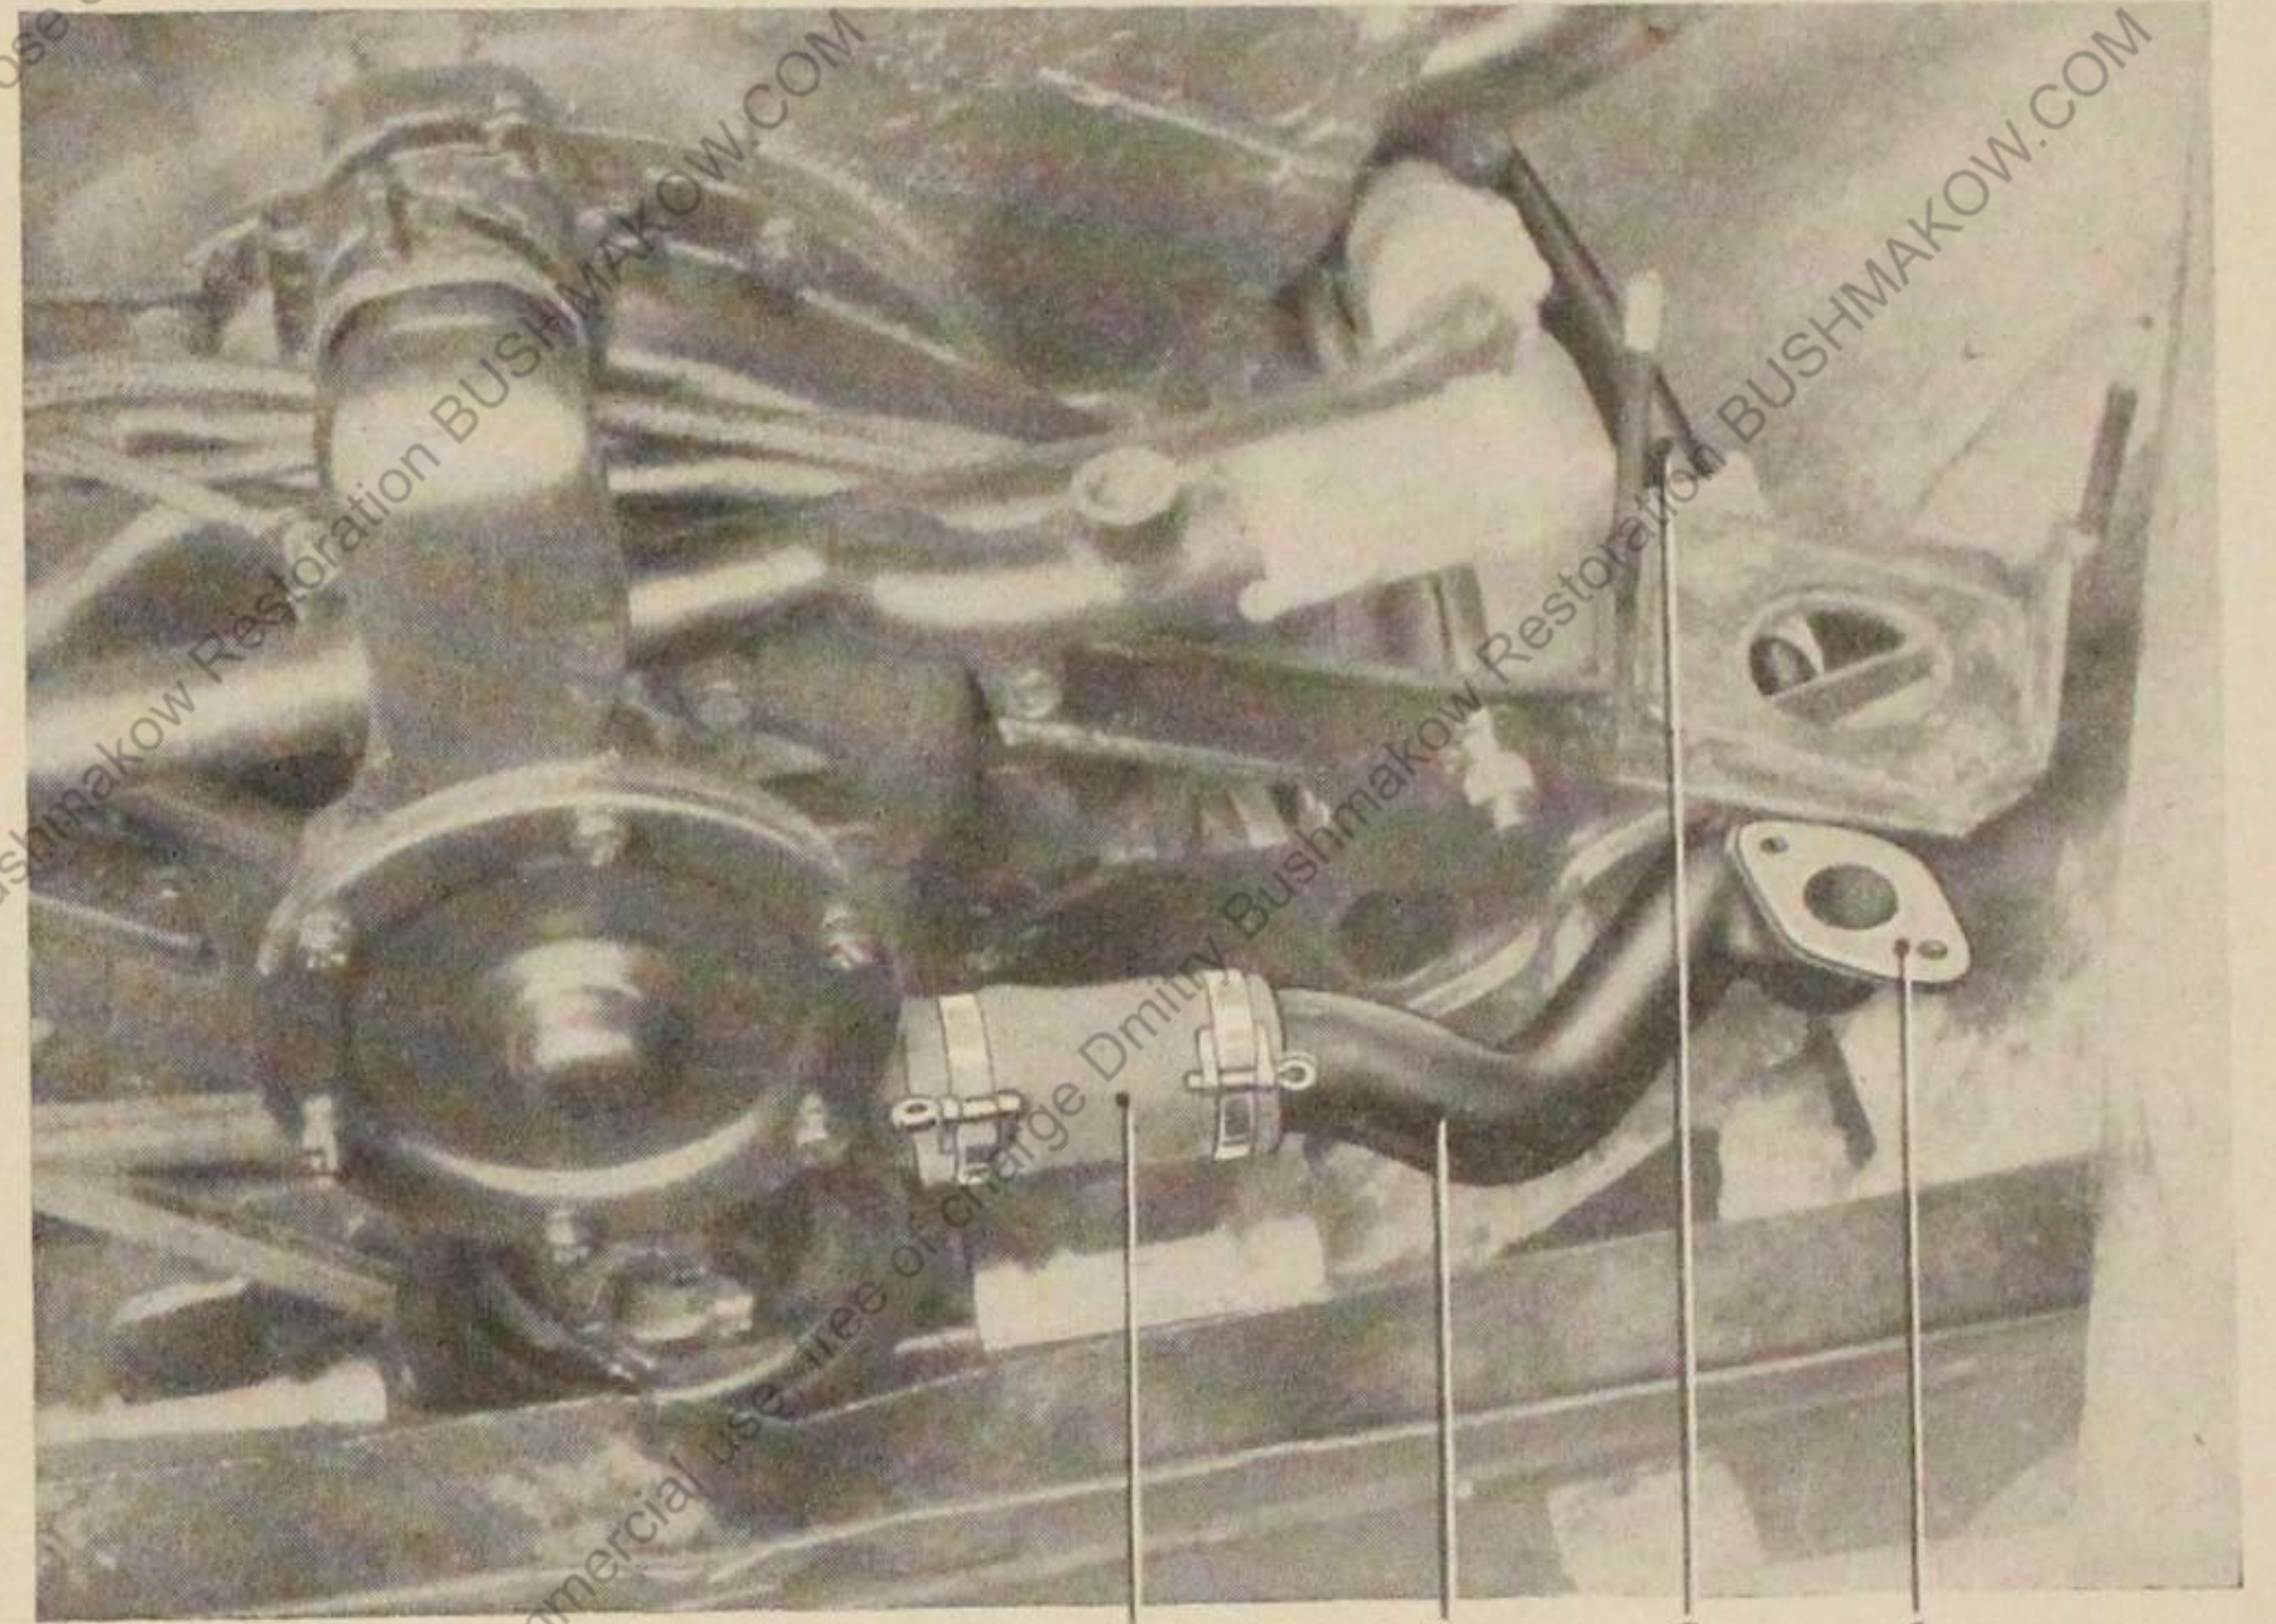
Verbindungsrohr zur Wasserpumpe einbauen
